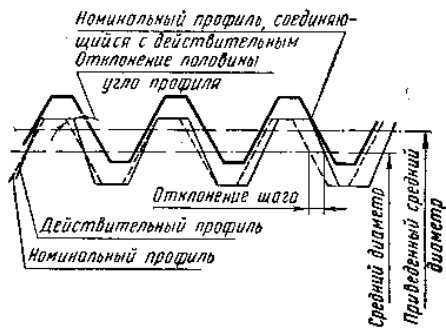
Номинальный и действительный профиль резьбы и отклонения
